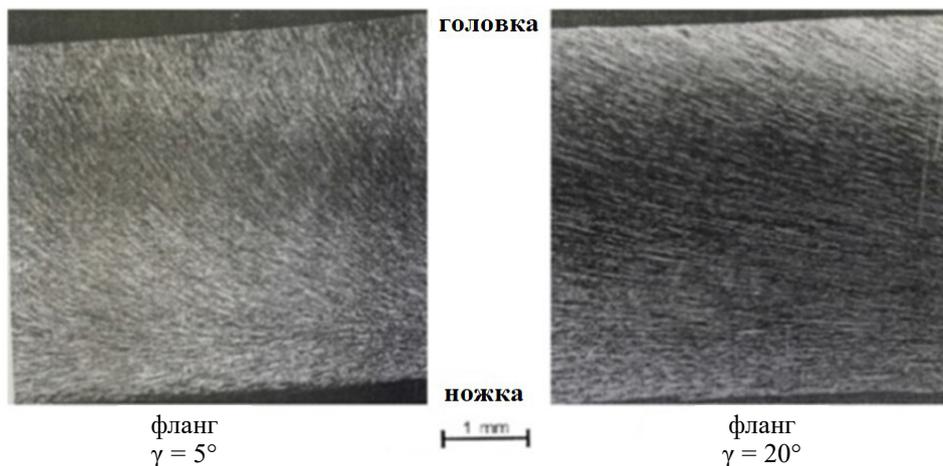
Направление фланка с углом обработки детали головки и ножки
